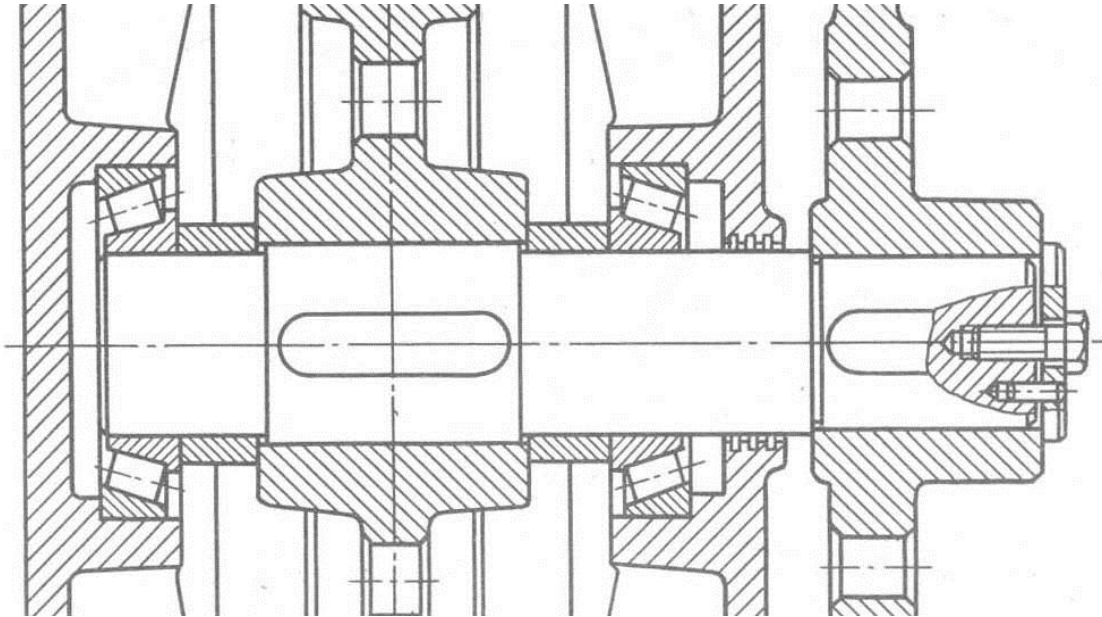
Складальний кресленник вузла вихідного валу редуктора
